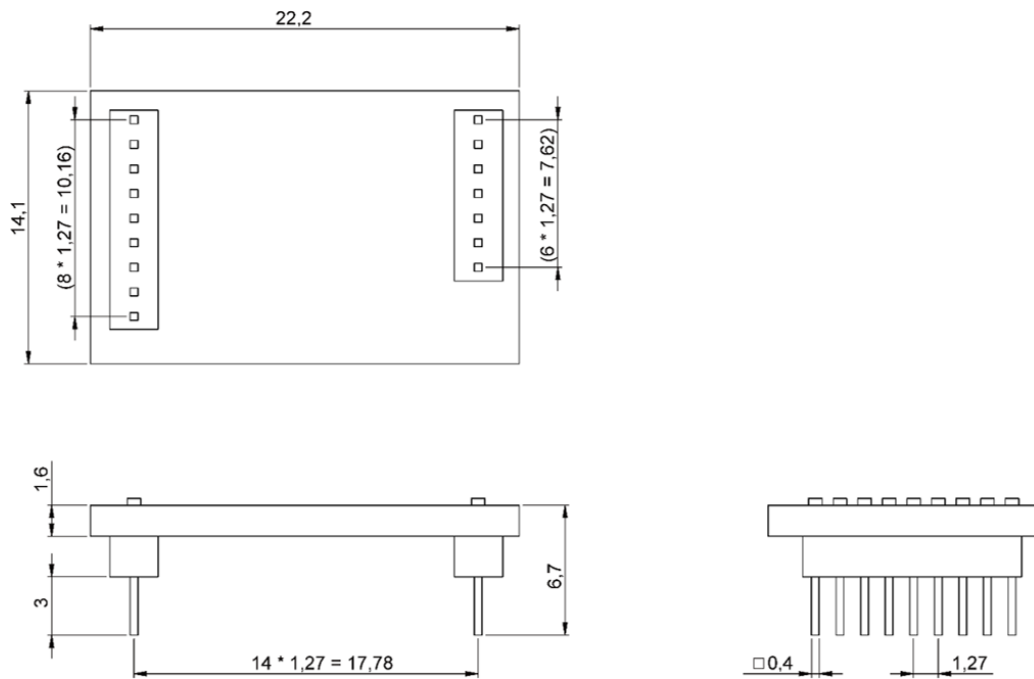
Dimensões da Shuttle Board 3.0 Padrão
